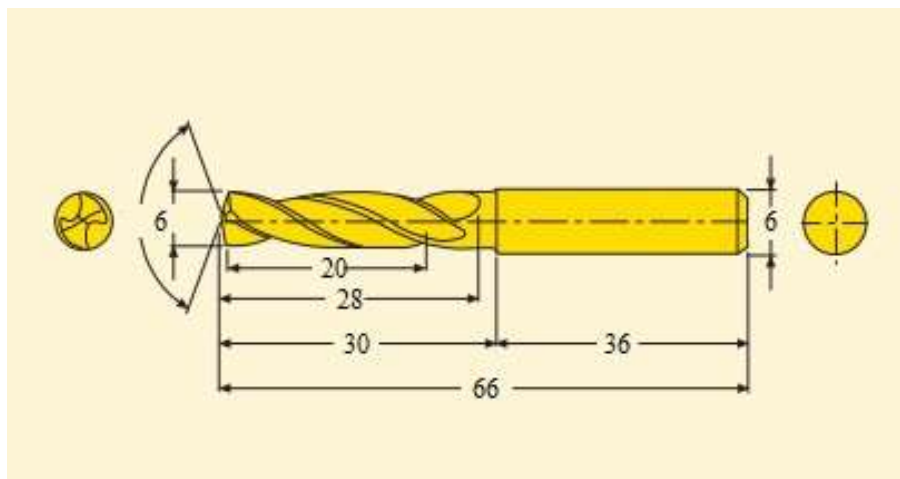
СверлоSecoUniversal – SD1103-0600-020-06R1
